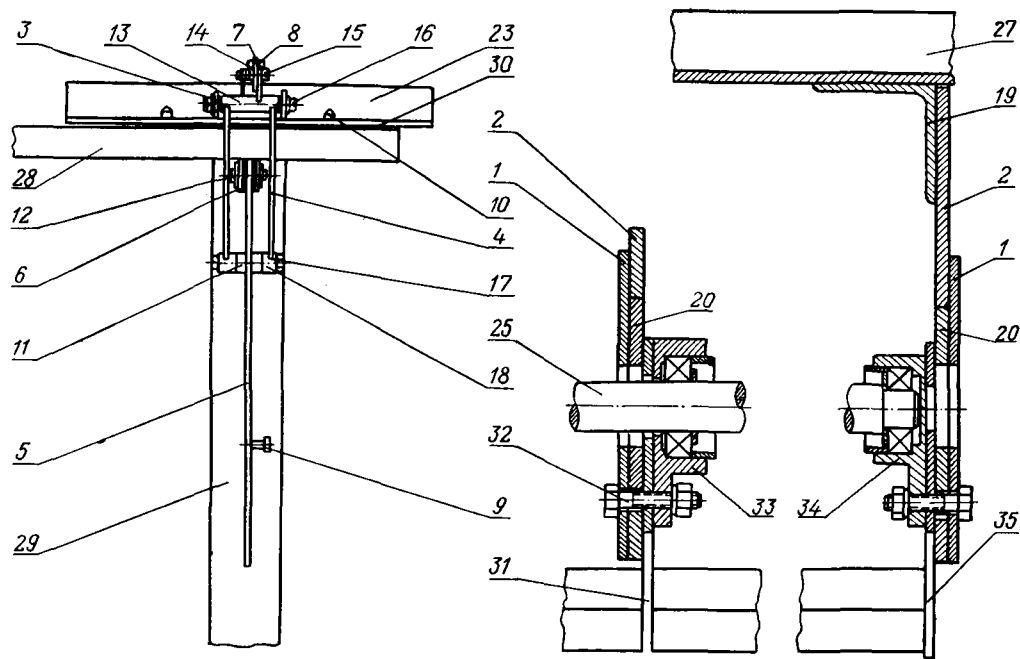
Узлы сборки деталей и их монтаж на комбайне:
